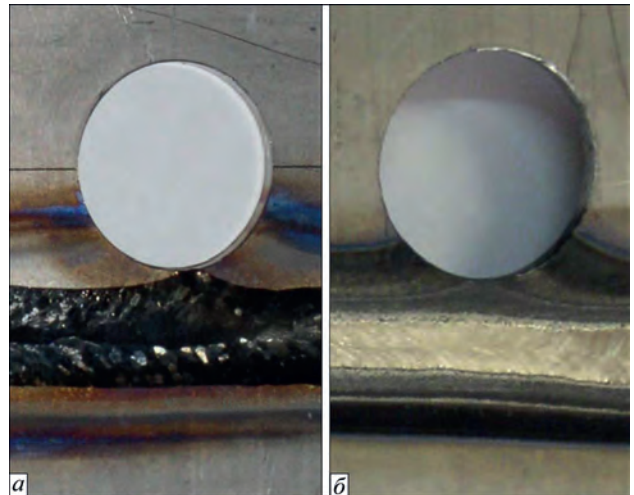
Зовнішній вигляд фрагментів зварних зразків-імітаторів зі сплаву ВТ-20 завтовшки $\delta = 2$ мм при повному проплавленні: а – TIG зварювання, струм зварювання – 100 А; б – A-TIG зварювання, струм зварювання 50 А
